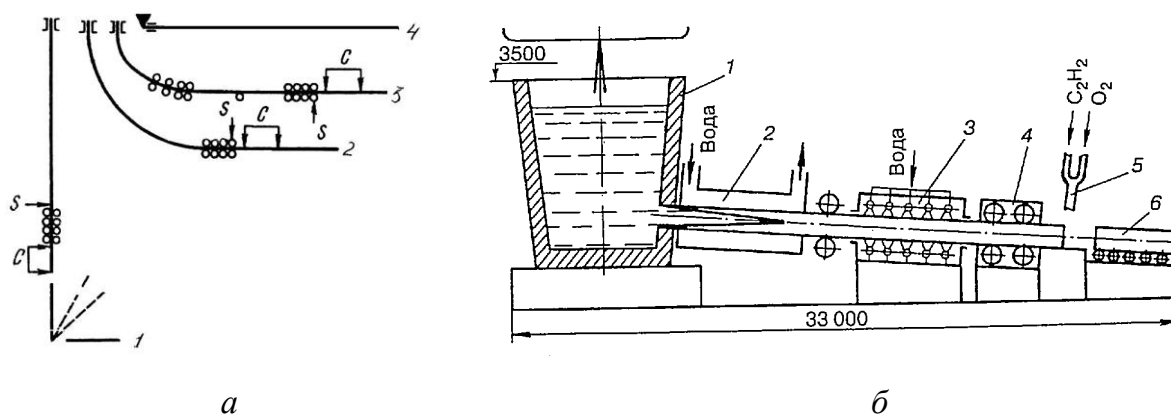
Схемы непрерывного литья заготовок:
